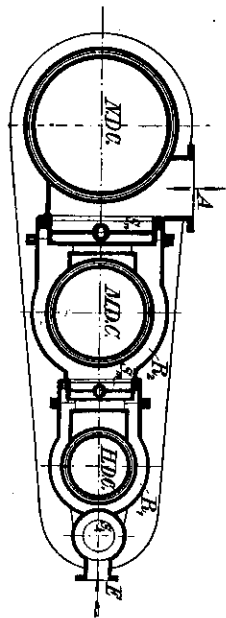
Niederdruck- Mitteldruck und Hochdruck- Zylinder.
